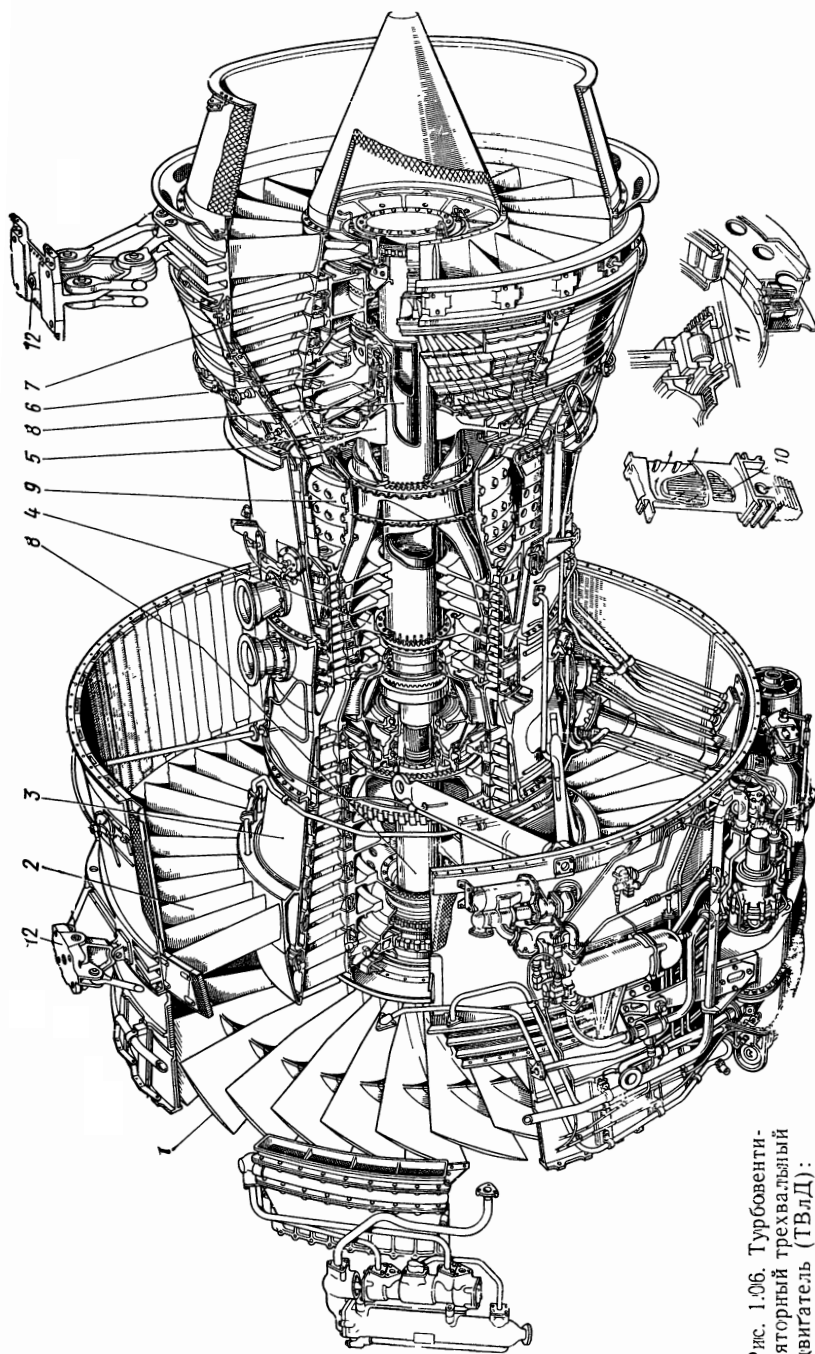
Турбовентиляторный трехвалный двигатель (ТВД):
